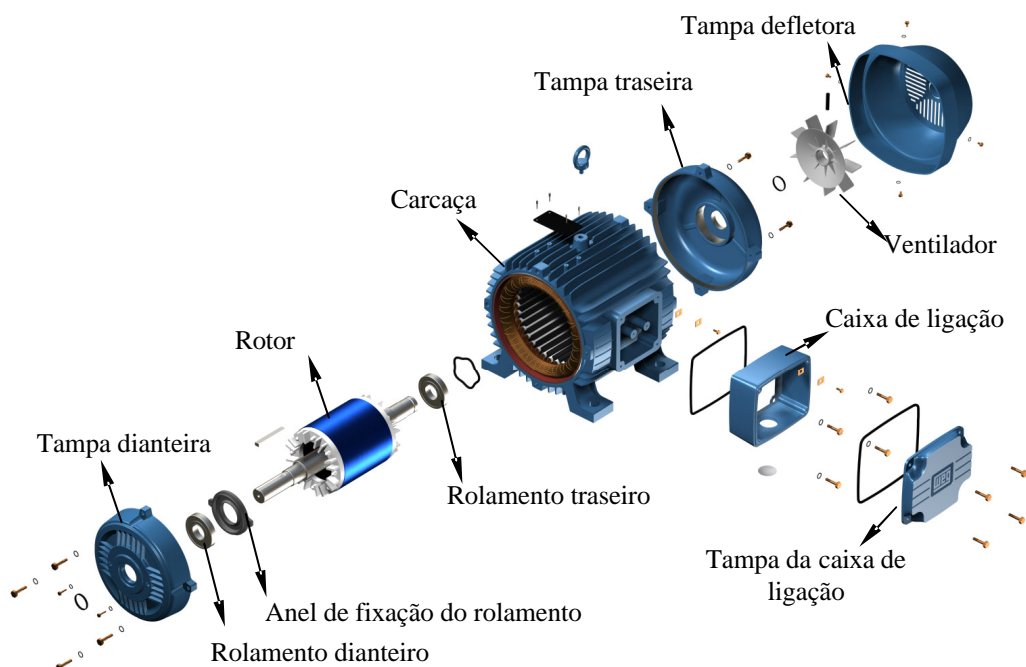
Vista explodida de um motor elétrico com carcaça totalmente fechada. Adaptado do Catálogo Geral de Motores Elétricos WEG (2006).
